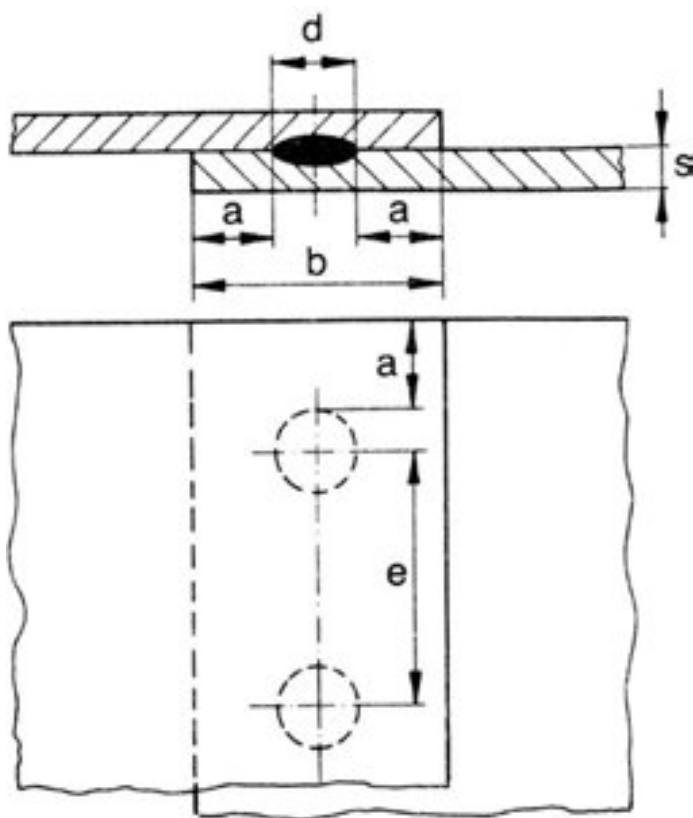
Геометрические параметры контактно точечной сварки:
